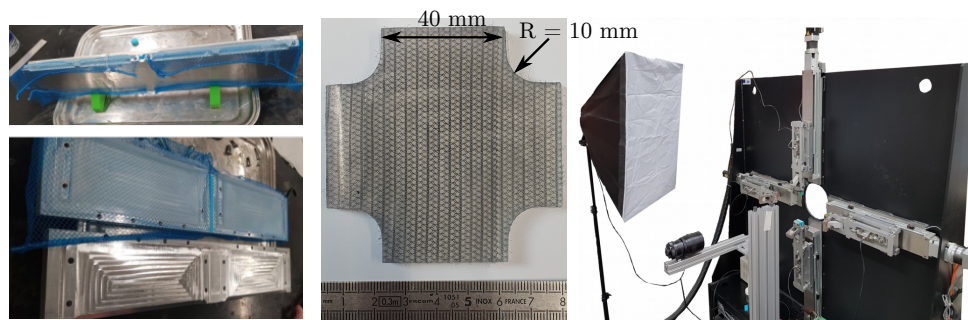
Fabrication d'une plaque composite. Eprouvette biaxiale et montage expérimental.
